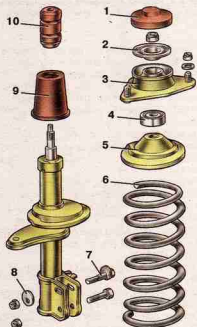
Элементы передней подвески: 1 – защитный колок; 2 – ограничитель хода сжатия опоры; 3 – верхняя опора стойки; 4 – подшипник верхней опоры; 5 – верхняя чашка пружины; 6 – пружина передней подвески; 7 – регулировочный болт; 8 – эксцентриковая шайба; 9 – защитный кожух; 10 – буфер хода сжатия
